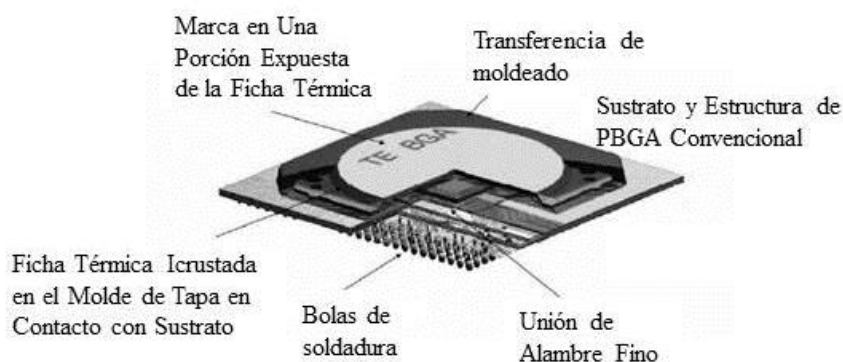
Esquemático de una base laminada de un paquete de BGA [2].
